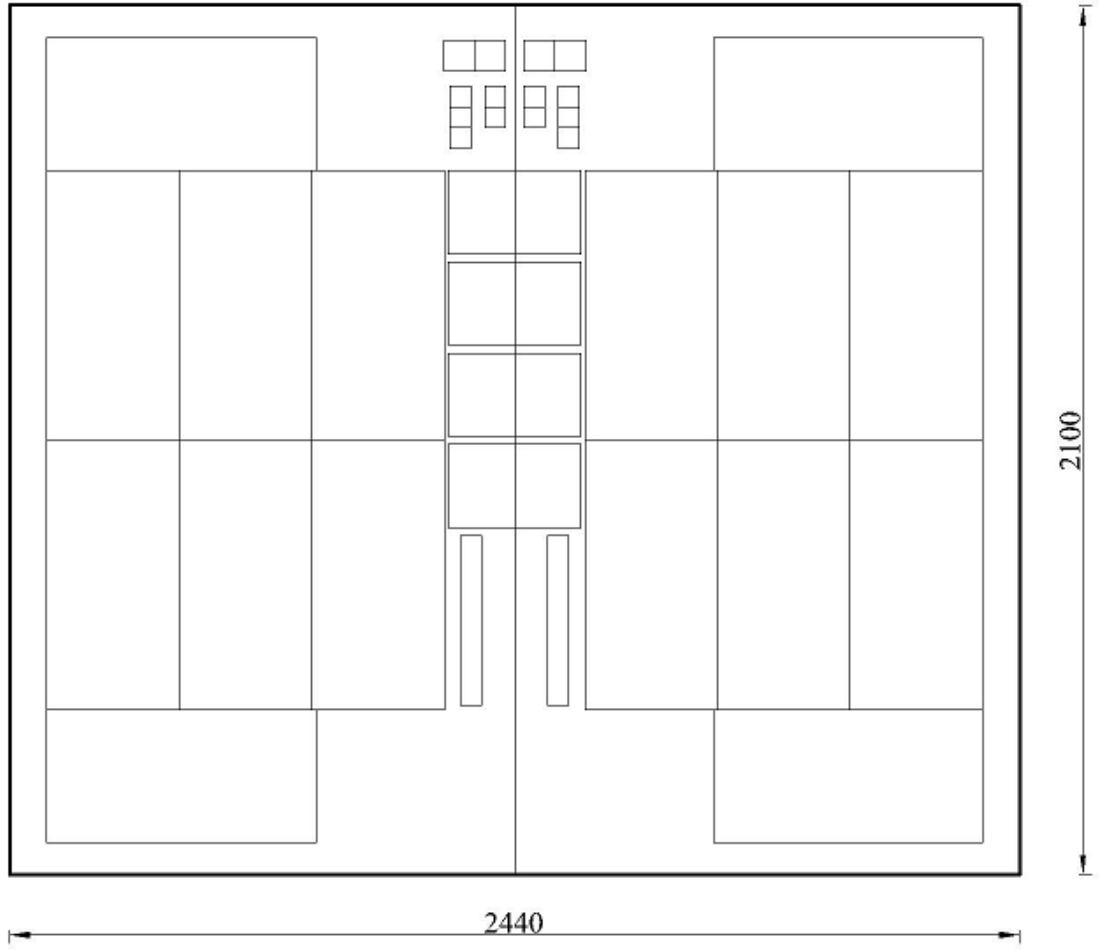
18 mm Yonga levha Kesim Planı (ölçüler mm)
